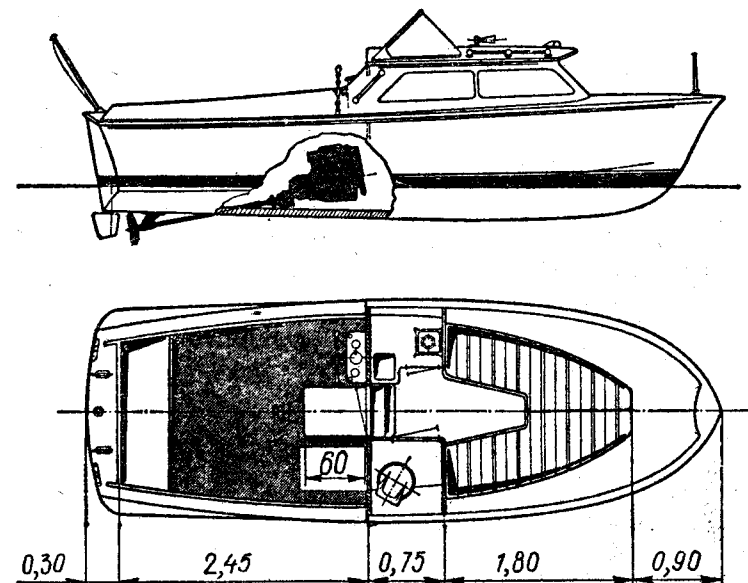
Обычный стационарный двигатель, расположенный почти в средней части катера, обеспечивает наиболее благоприятный дифферент.
